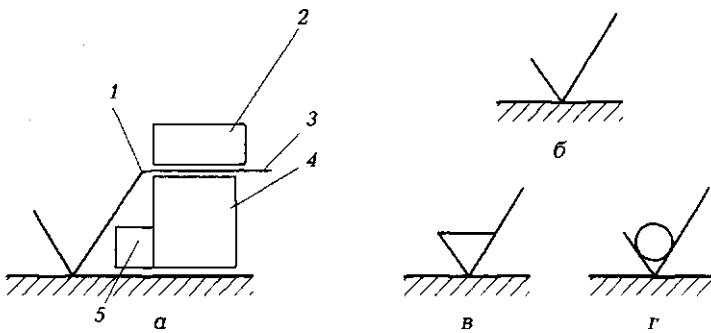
Условное обозначение шероховатости поверхности на чертежах:
